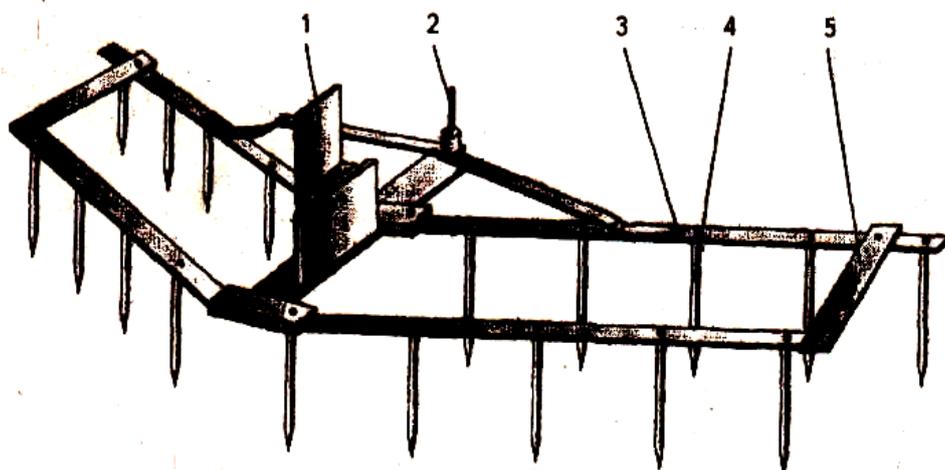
Зубовая борона бн-90: 1 – стойка; 2 – рукоятка; 3 – планка поперечная; 4 – зуб; 5 – планка продольная
